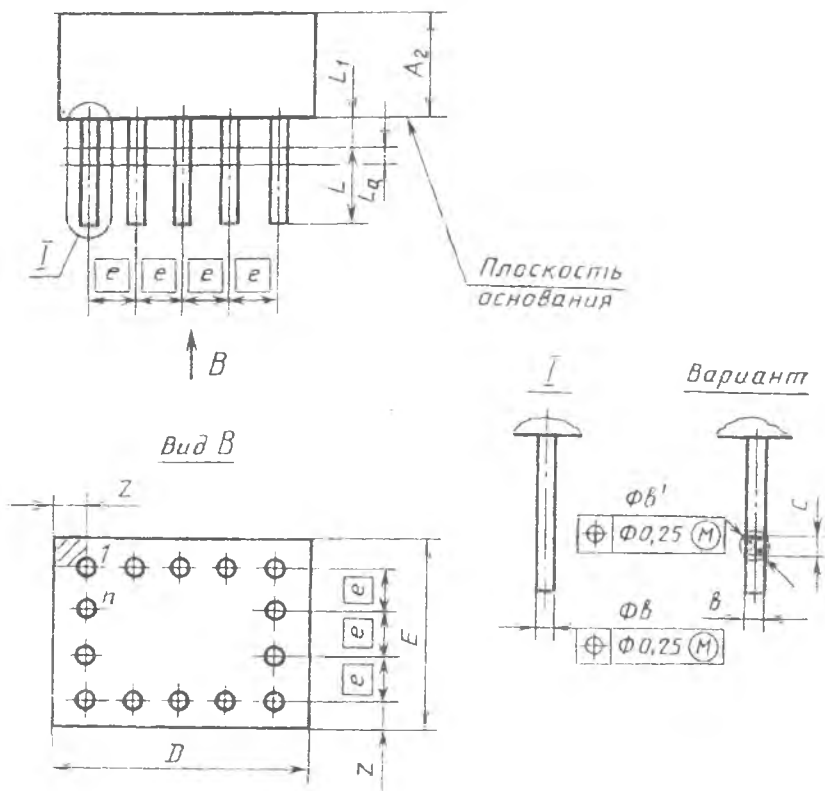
Конструкция корпуса типа 1 подтипа 4
